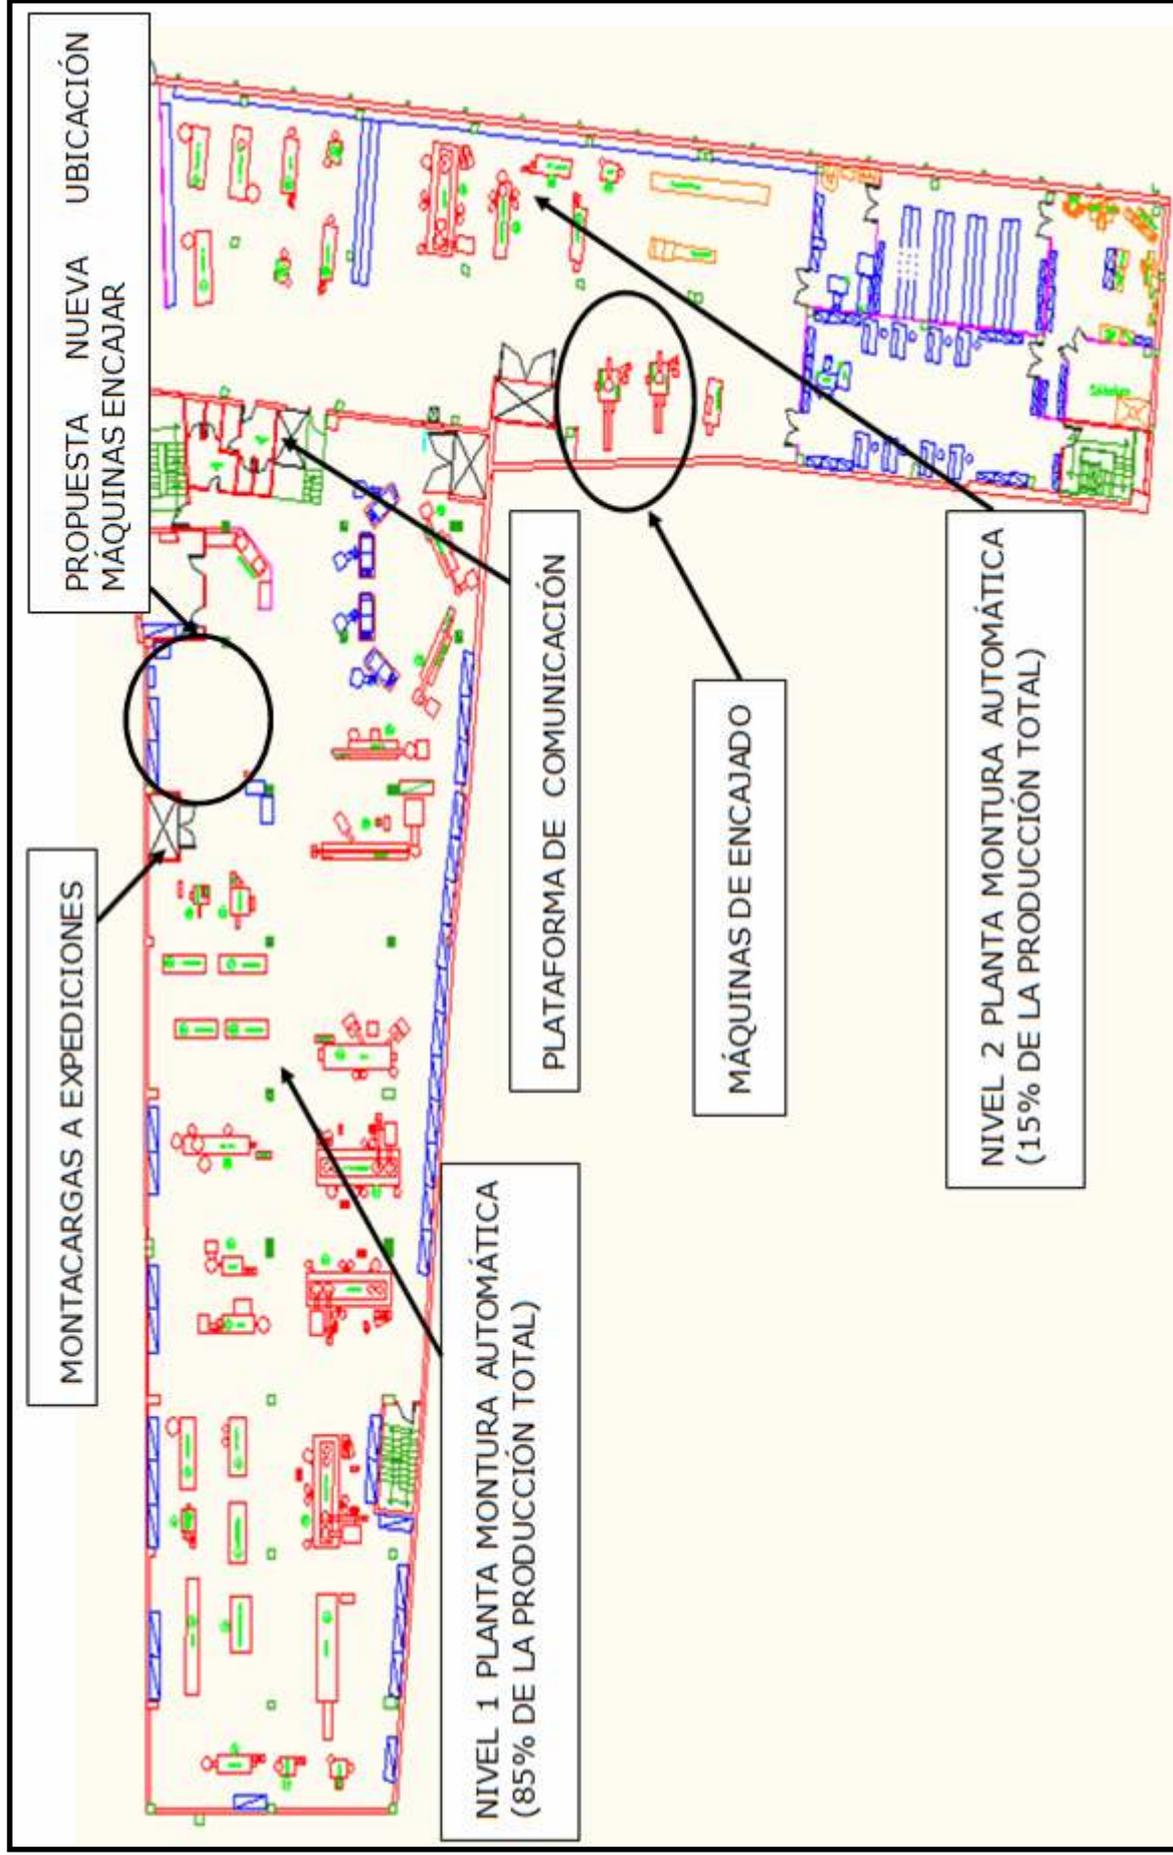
Planta de montura automática actual con especificaciones para modificar distribución.
